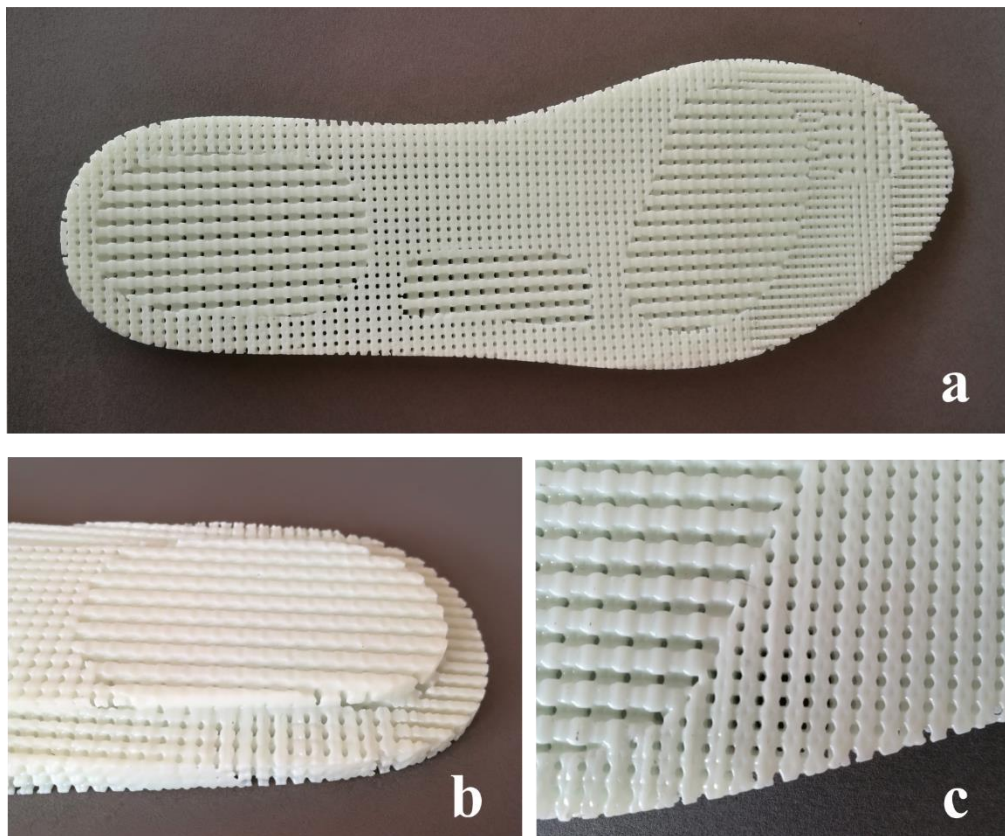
Entressola impressa, a) vista de cima, b) pormenor da parte de baixo zona do calcanhar, c) pormenor *lattices*.
